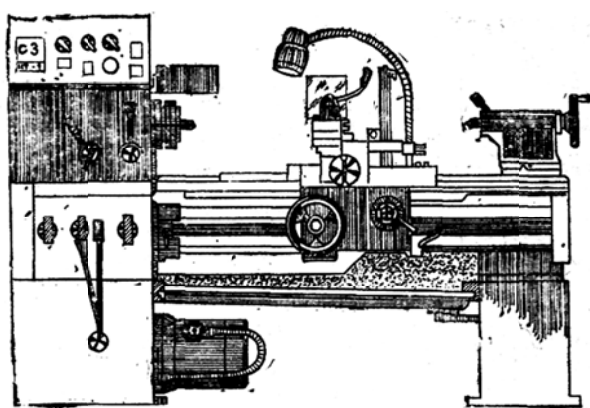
Токарно-винторезный станок, мод. ИТ-1М
